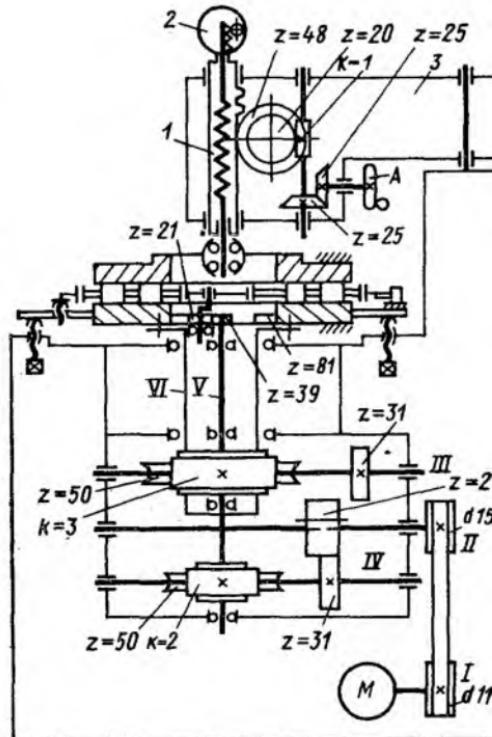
Кинематическая схема двухдискового вертикально-доводочного станка 3Б814
